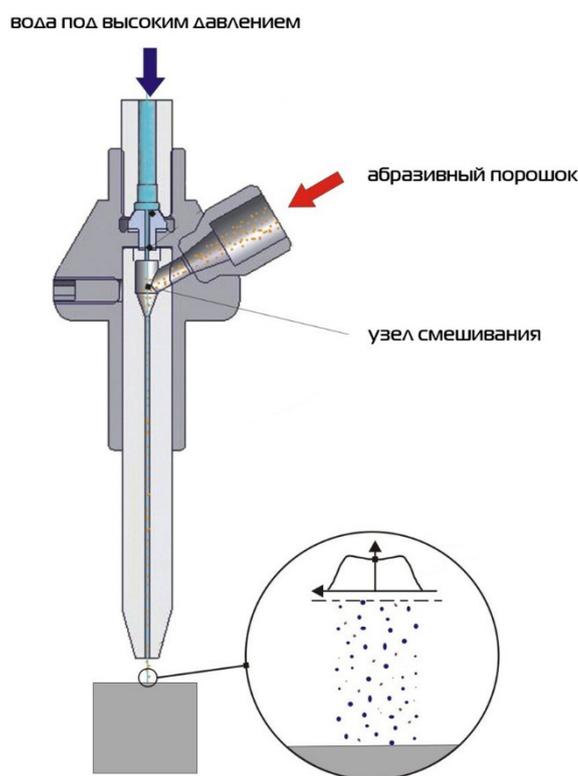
Схема устройства рабочей части установки гидроабразивной резки
